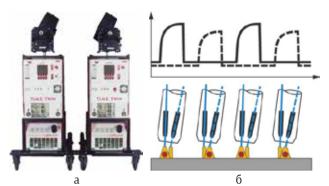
Установка для двухдуговой автоматической сварки «Time Twin» плавящимся электродом (а) и принцип реализации тандемной сварки (б)
